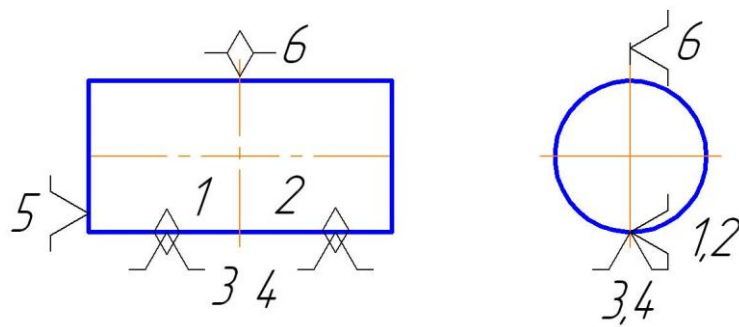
Теоретична схема базування при обробці шпонкових пазів на вертикально-фрезерному верстаті
